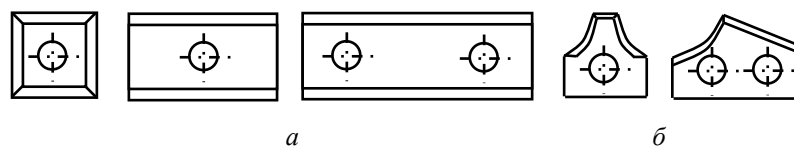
Режущие пластины: *a* – поворотные; *б* – профильные
